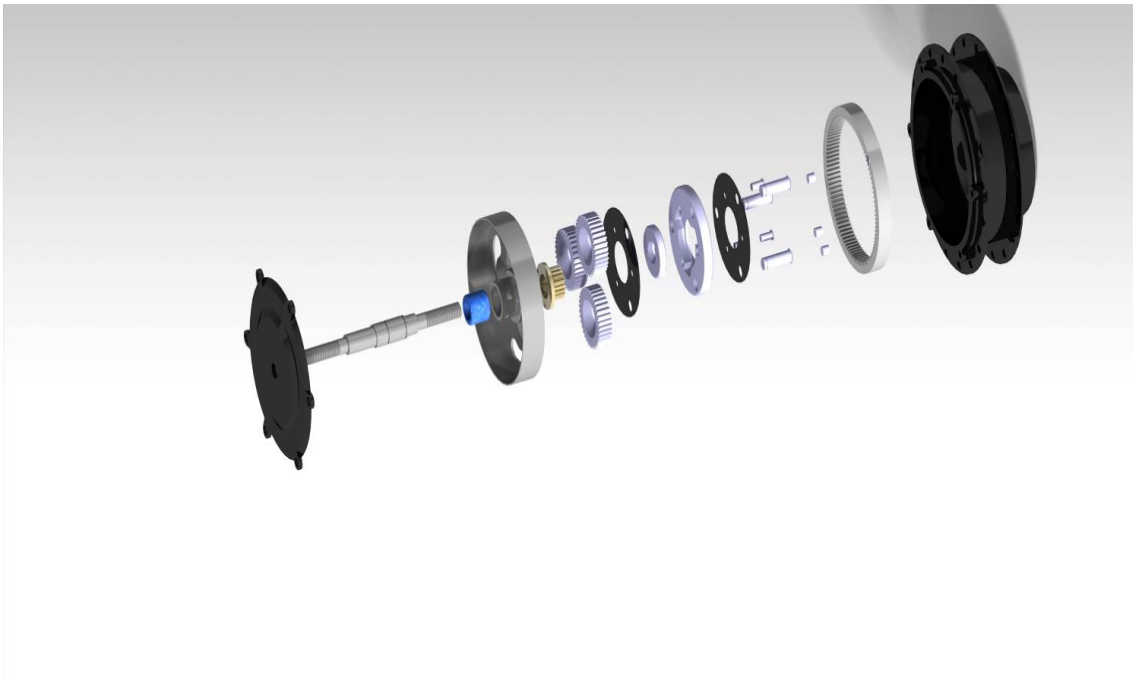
Explosionado del motor (Fuente: elaboración propia)
